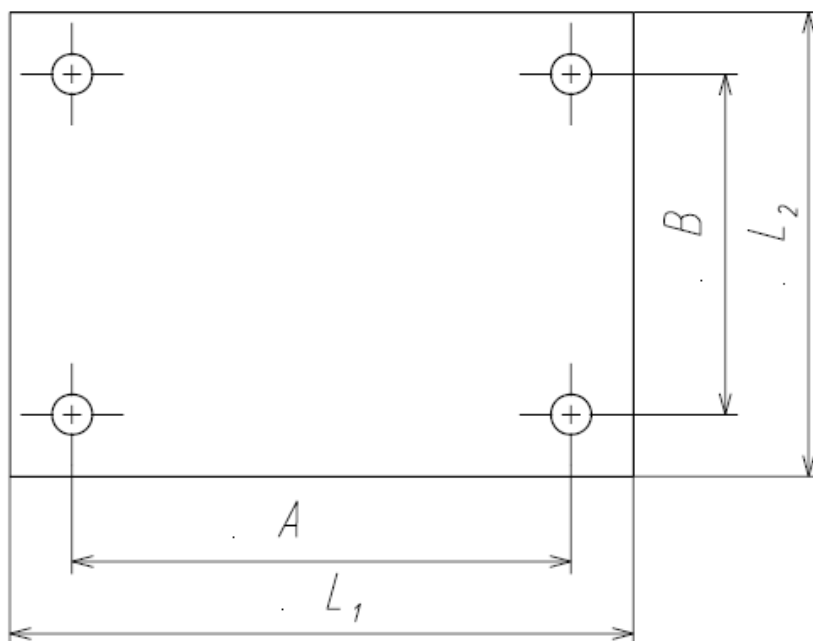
Эскиз детали «Крышка», вариант 1.
